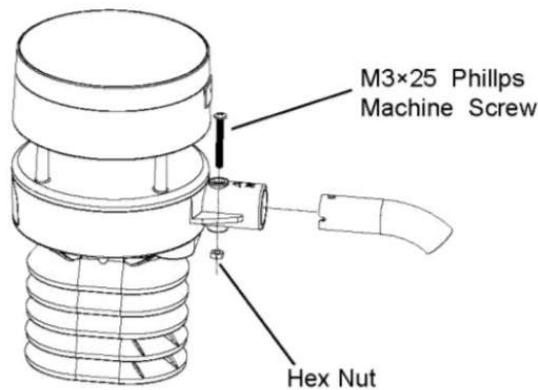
schema di montaggio del pacchetto del sensore 5-3
